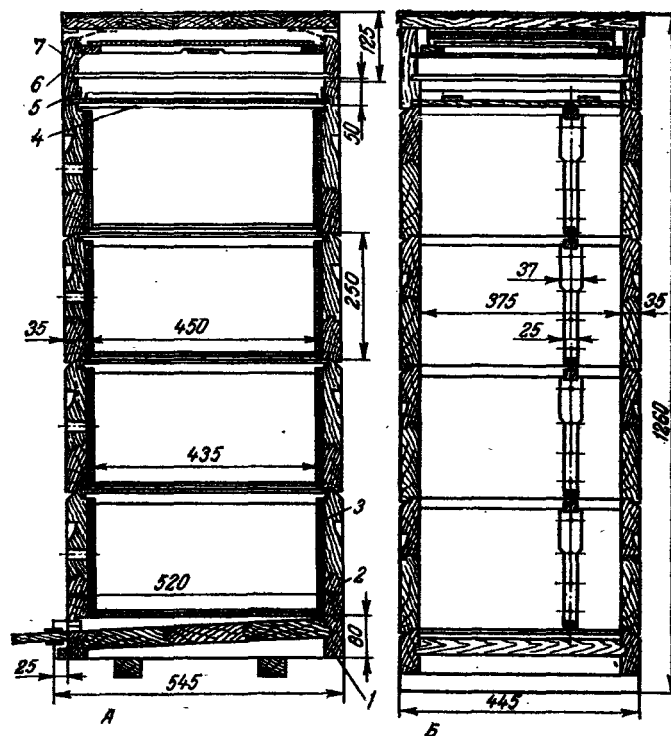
Многокорпусный улей (А — разрез вдоль рамок, Б — разрез поперек рамок):
